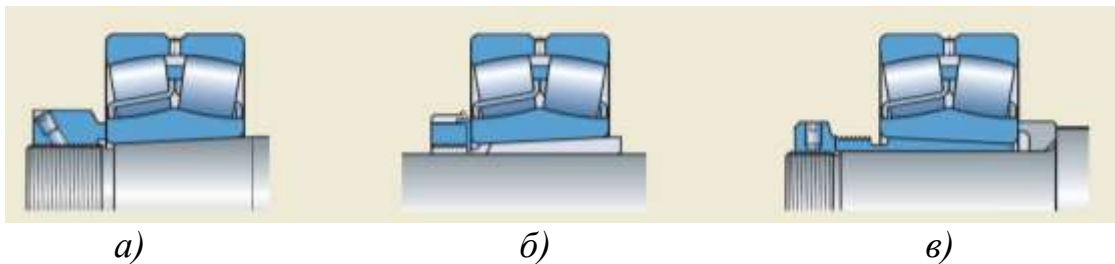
Закріплення підшипника на посадковій шийці валу або на втулці
